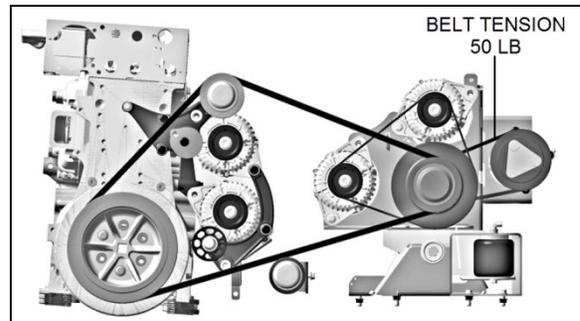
DISTRIBUCIÓN DE BANDA CON COMPRESOR DE A/C PEQUEÑO SERIE h3-45 VIP 22380
